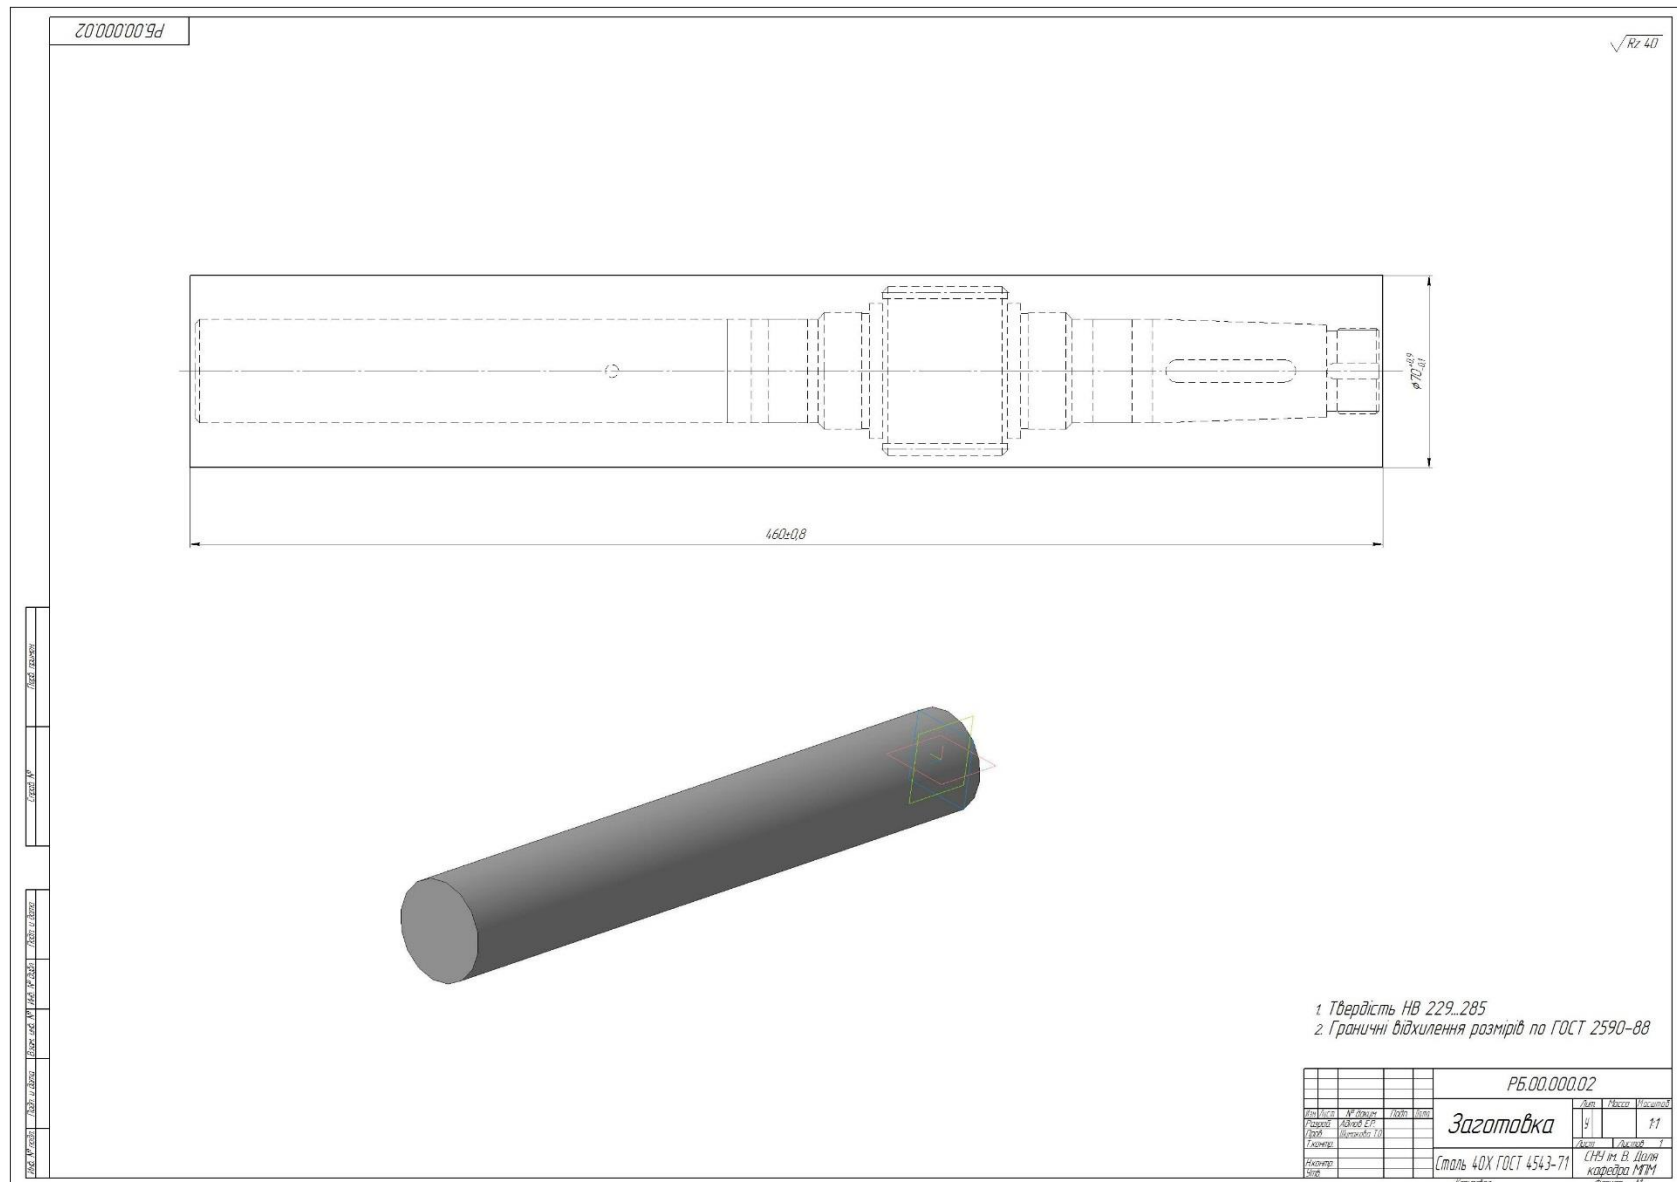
Кресленик заготовки деталі «Вал шестерня» приводу насосу
